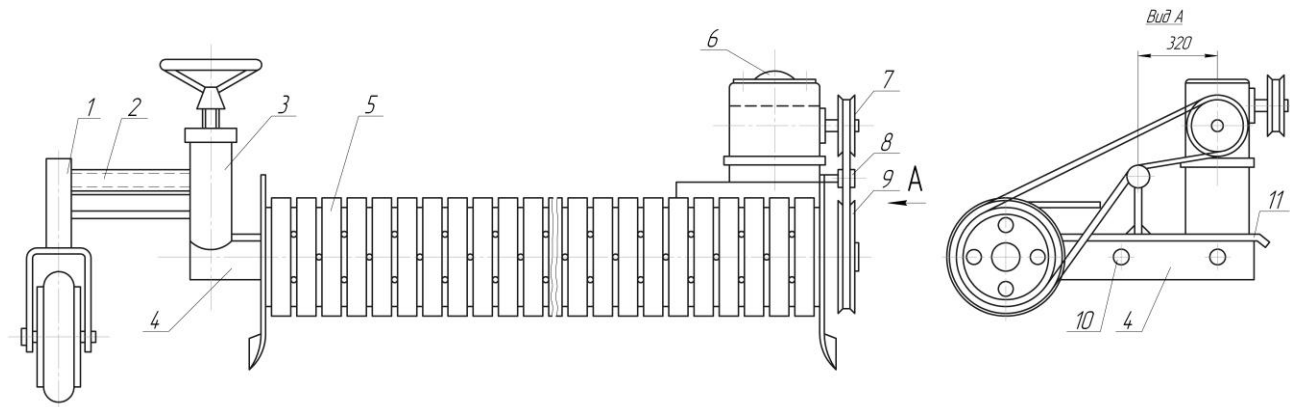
Схема пристрою для просушування валків: 1 – кронштейн; 2 – тяга; 3 – регулювальний штурвал; 4 – брус; 5 – підбирач; 6, 7, 9 – шківи; 8 – натяжний ролик; 10 – виступ відрізки труби; 11 – металевий лист.
